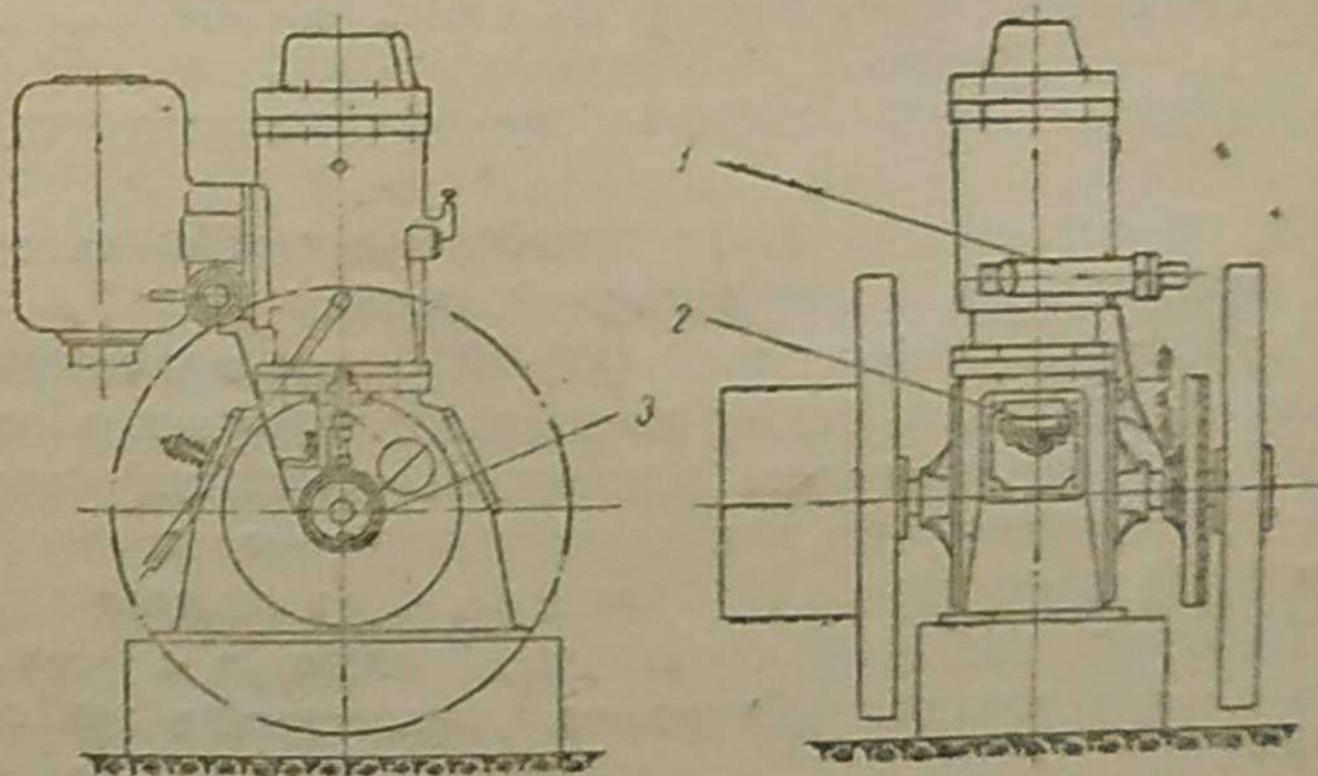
Двухтактный нефтяной двигатель, переоборудованный для работы на газе:
